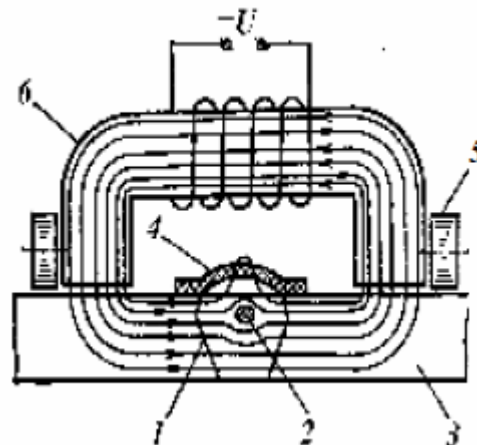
Схема намагничивания сварного шва вместе с магнитной лентой:
